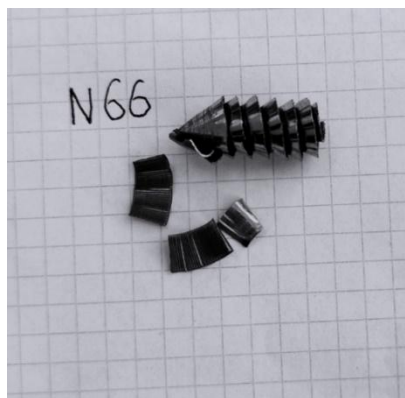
Стружка, полученная при сверлении заготовки № 66
